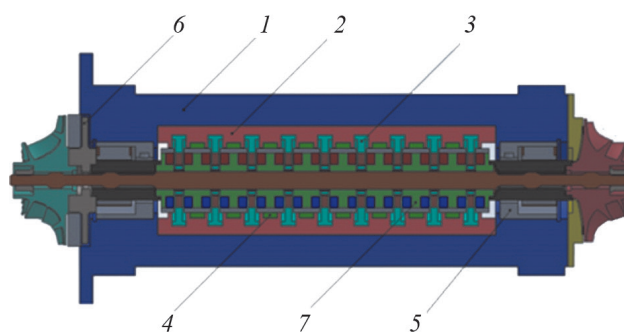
Поперечный разрез аксиального генератора с указанием расположения основных конструктивных элементов: 1 – станина; 2 – кассета статора; 3 – обмотка якоря; 4 – радиальный газодинамический подшипник; 5 – радиальный активный магнитный подшипник; 6 – осевой газодинамический подшипник; 7 – индуктор
